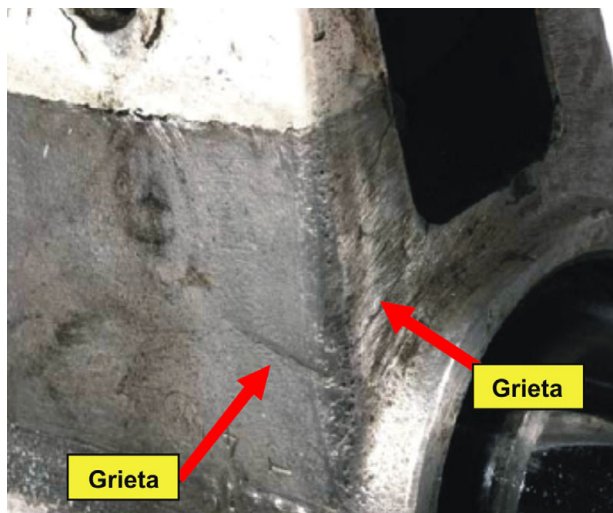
Fotografía de la grieta en la pieza de la pata derecha
